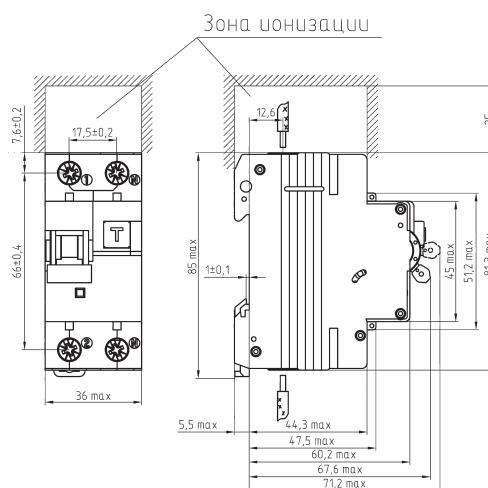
Габаритные, установочные и присоединительные размеры АВДТ
